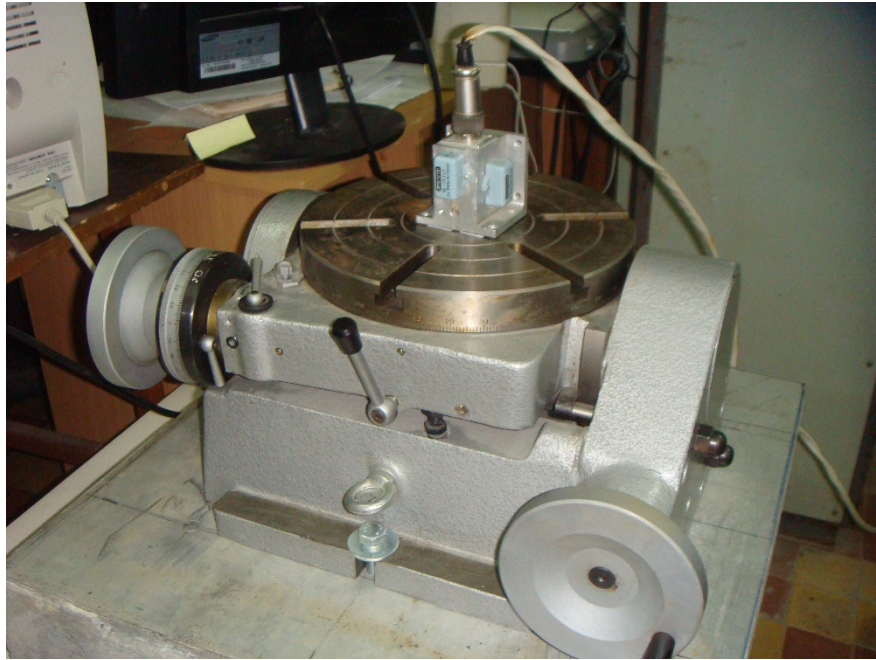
Поворотний стіл OSN-250 "PROMA CZ"
